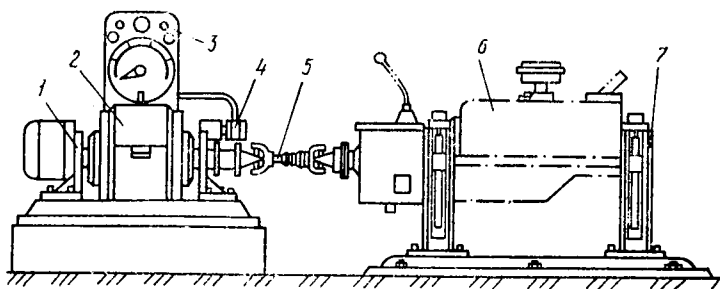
Электротормозной стенд для обкатки и испытания двигателей:
